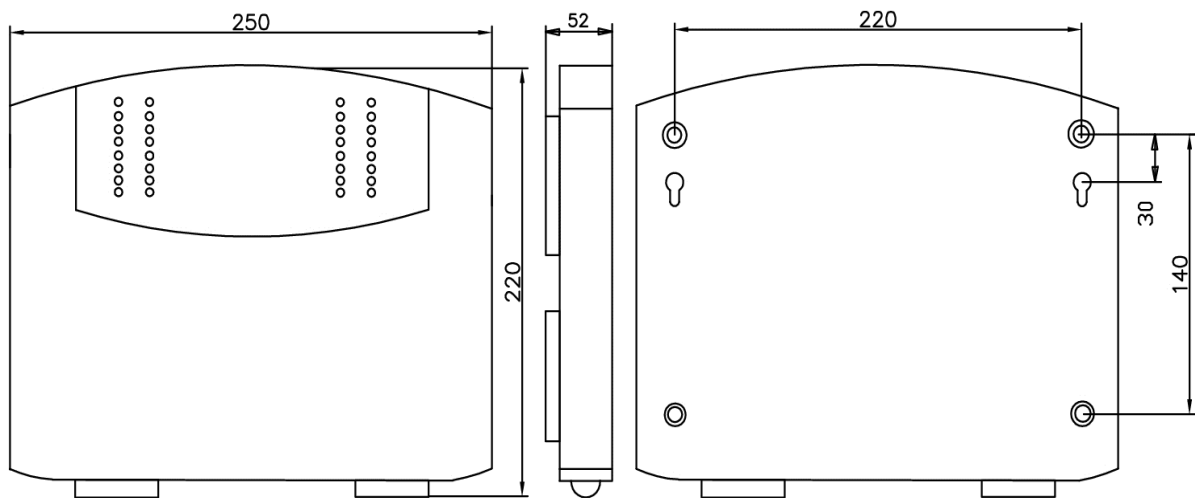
Габаритные и установочные размеры прибора, пластмассовый корпус
